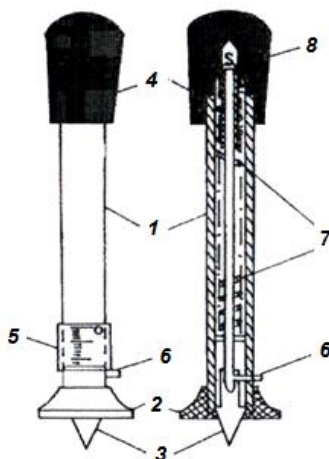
Мікропенетрометр МВ-2: 1 – корпус; 2 – опорний диск; 3 – плунжер; 4 – ручка; 5 – циліндричний повзун; 6 – шпилька з'єднання плунжера зі штоком; 7 – пружина; 8 – гайка регулювання
